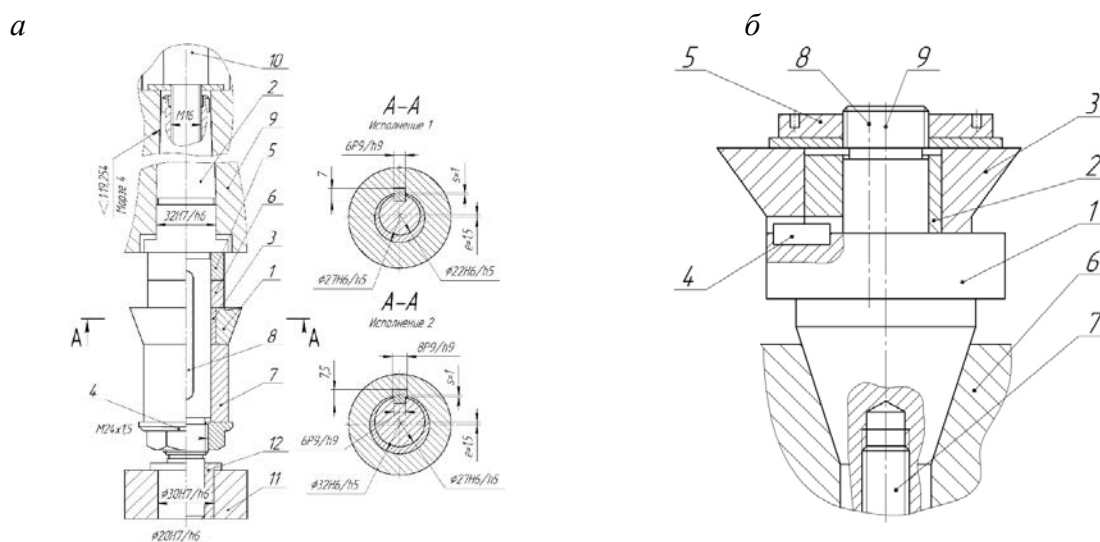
Инструменты для обработки синусоидальных поверхностей:
